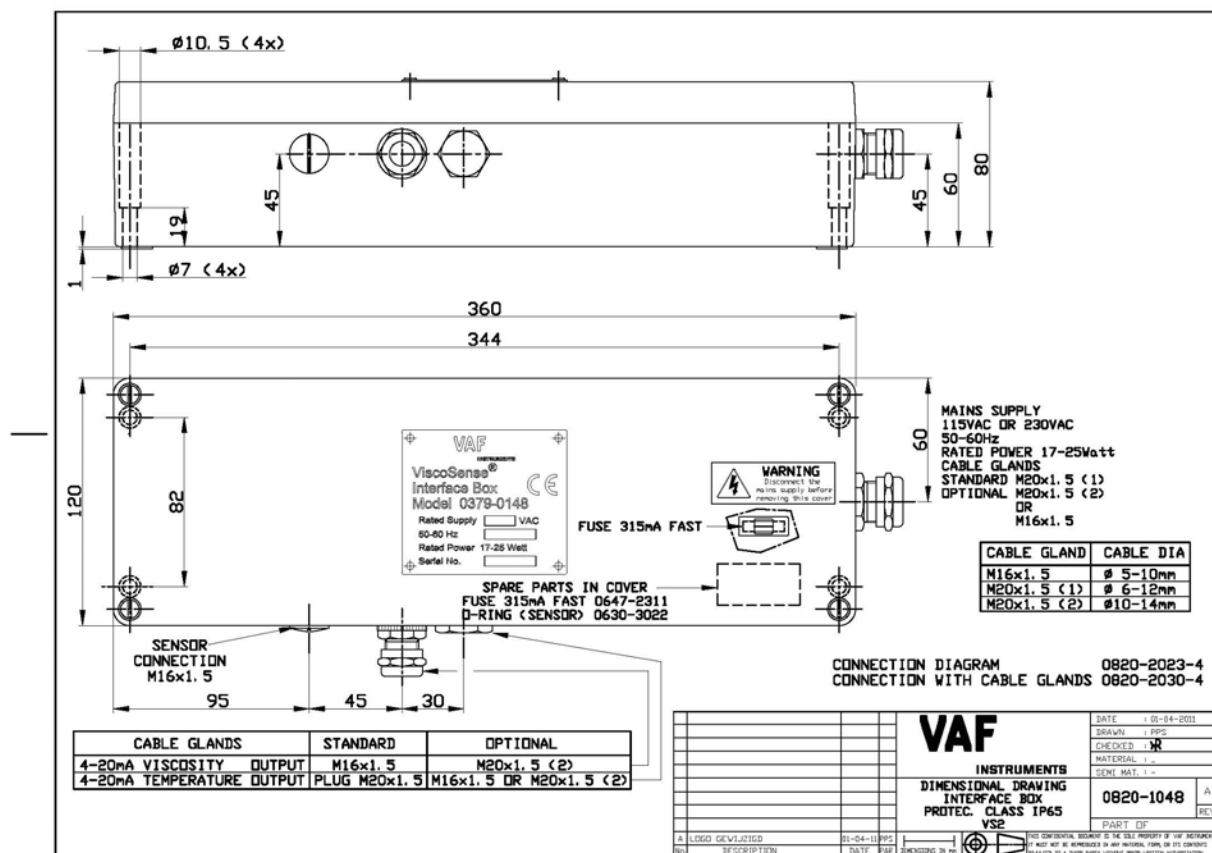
Dimensioni della box di interfaccia ViscoSense®2 (Tutte le dimensioni sono in millimetri).
